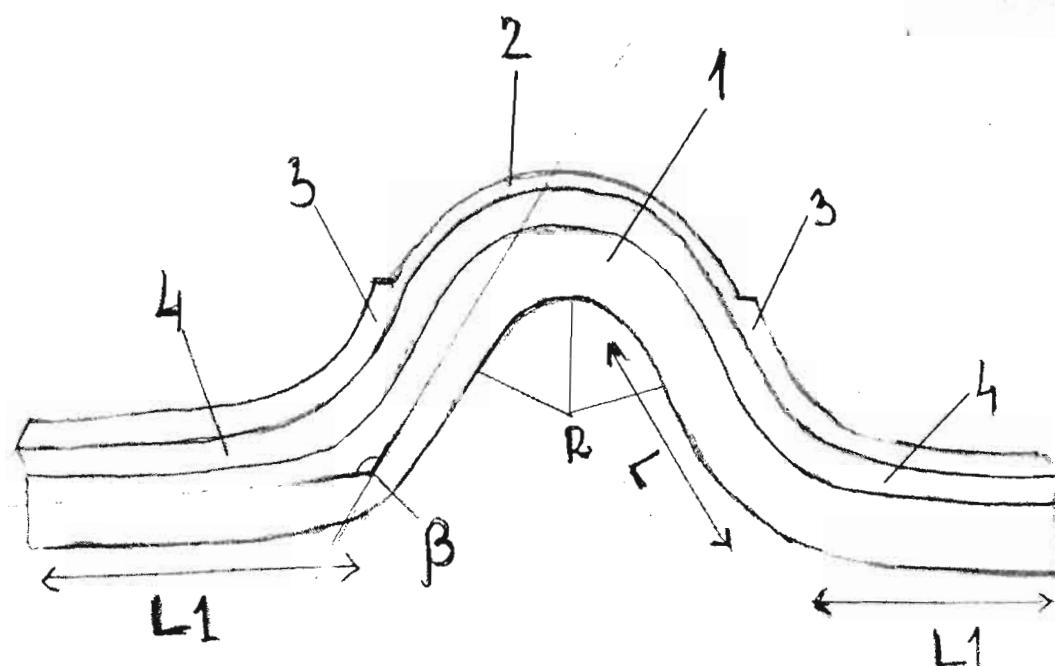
Vedere frontală a dispozitivului montat pe o mască de protecție;
